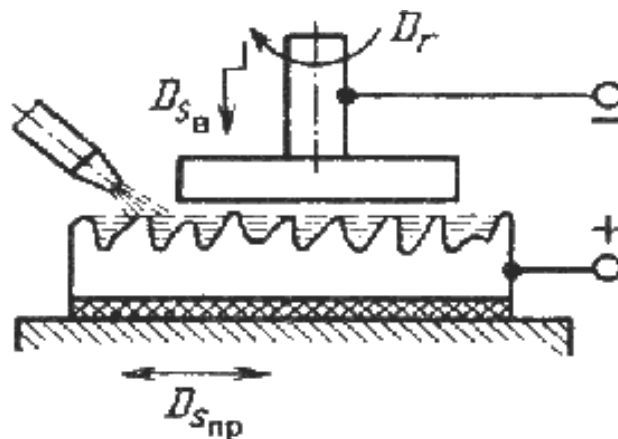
Схема анодно-механической обработки плоской поверхности
